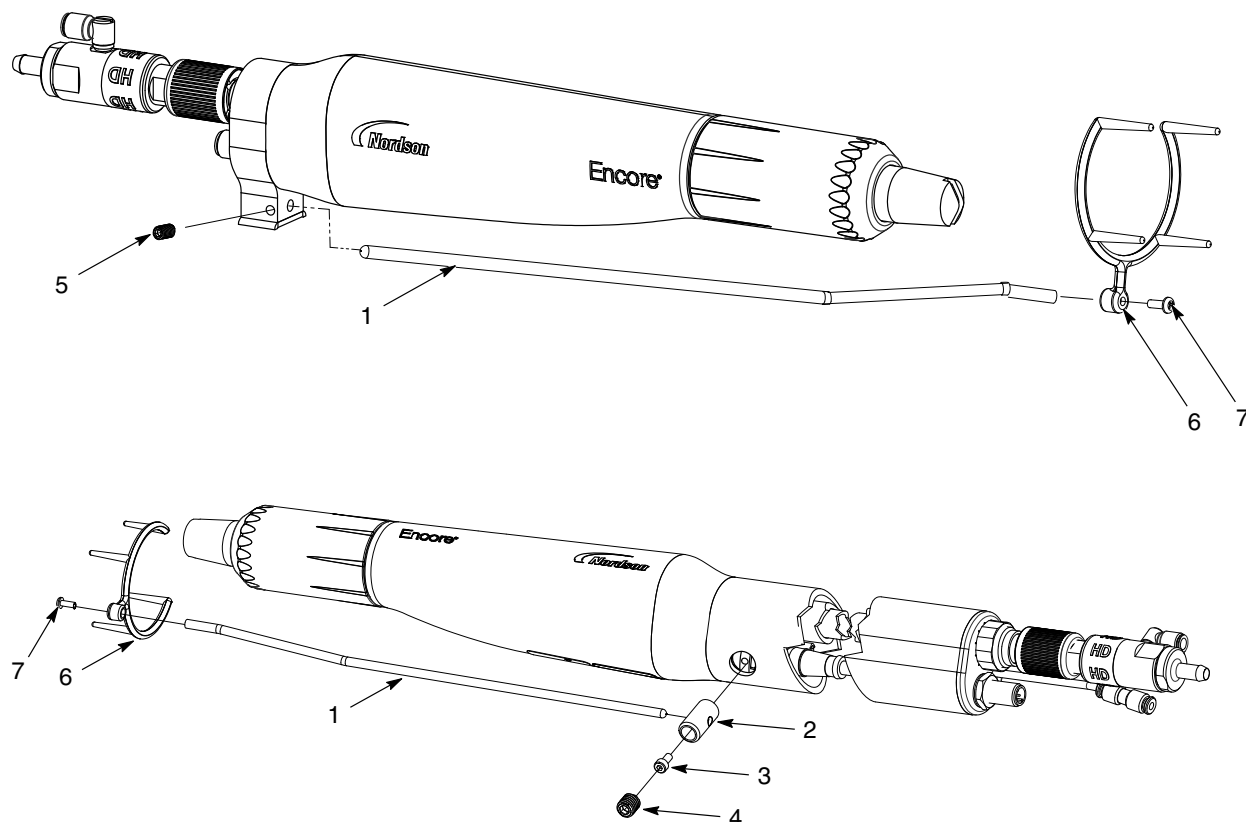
Pistoolstang voor stangbevestigde pistolen
